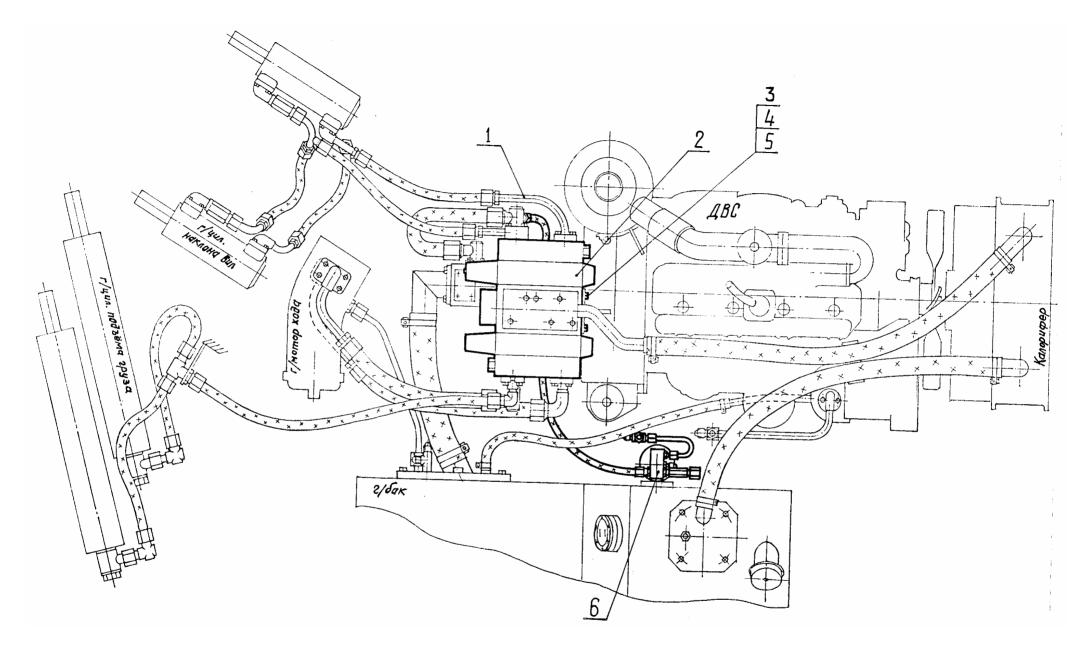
Гидрооборудование Fig. 19 Hydraulic Equipment
